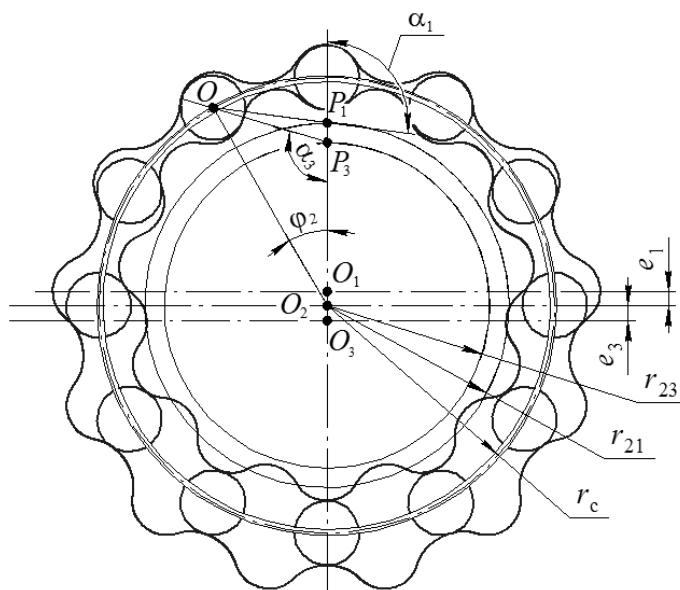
Схема двухполосного зацепления передачи с промежуточными телами качения и свободной обоймой
